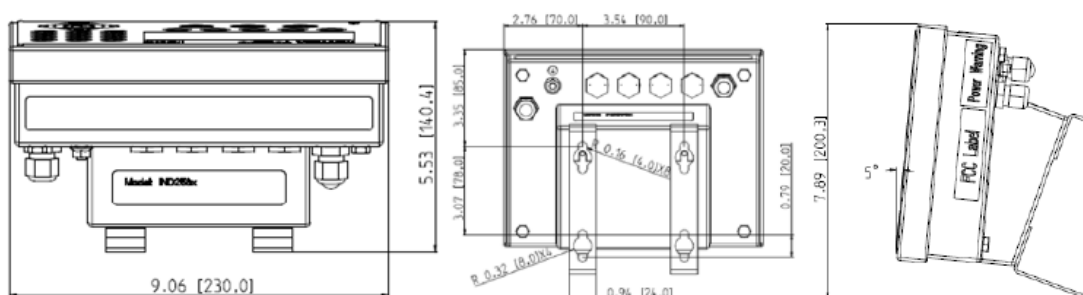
IND256x 支架安装尺寸 – 墙式安装和立柱安装
